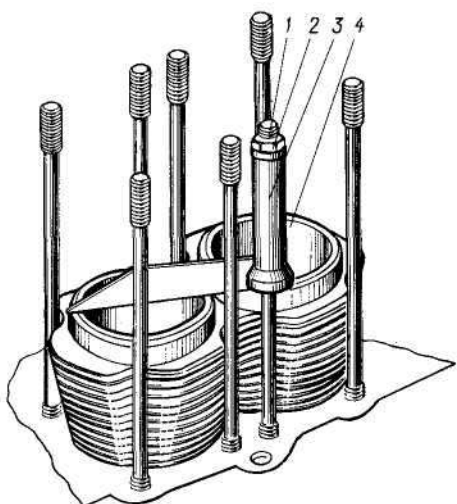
Приспособление для фиксации цилиндров на картере коленчатого вала:
